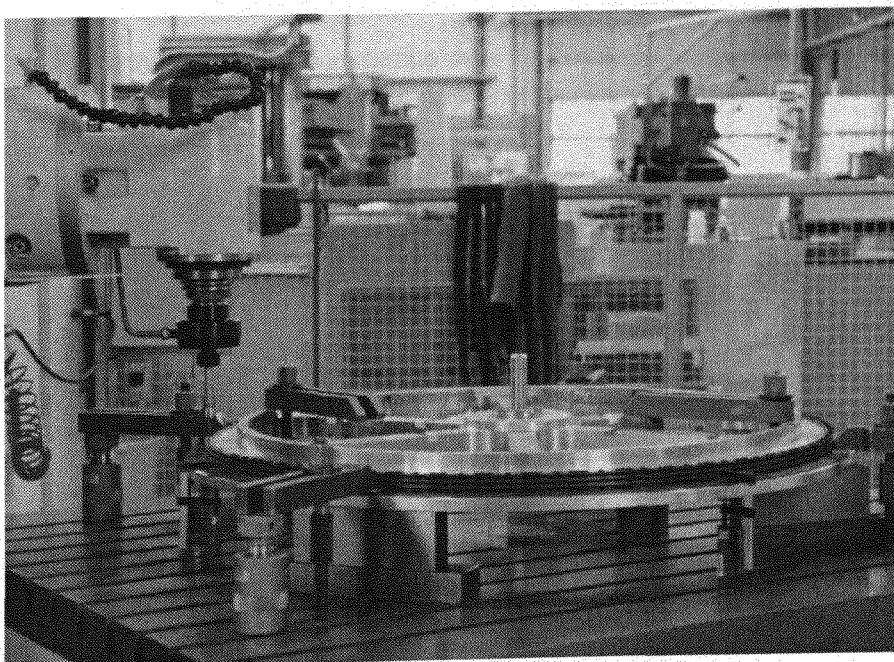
Alu-Speichenrad und Carbon-Nabe auf dem Bohrwerk
